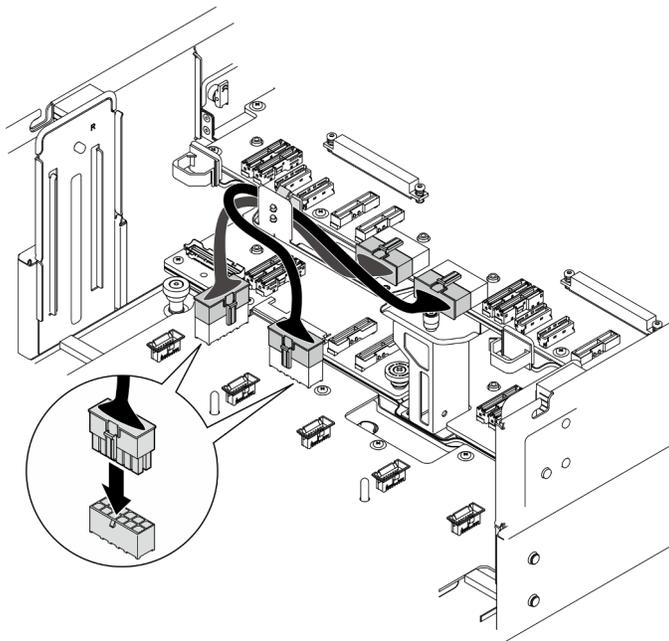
Anschließen der Kabel der Stromversorgungsplatine
